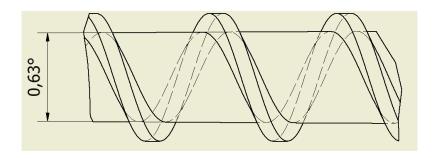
Filete para Husillo de máquina de extrusión y soplado
